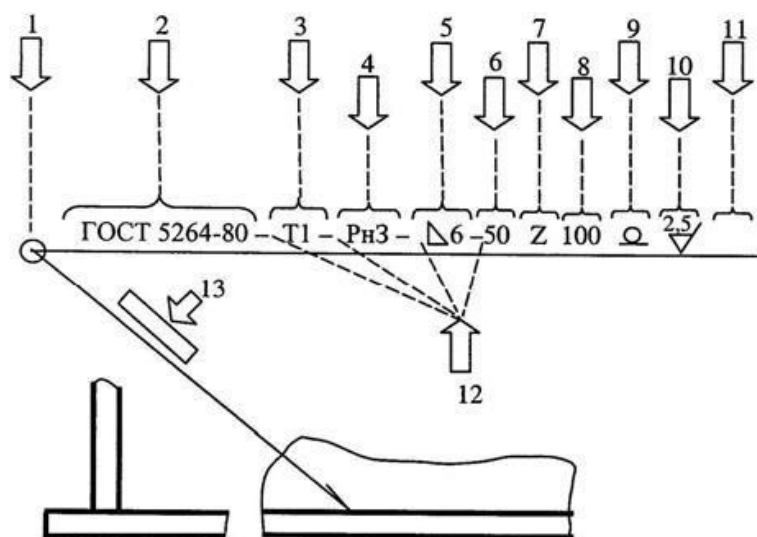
Структура обозначения шва: 1 – шов по замкнутому контуру; 2 – номер стандарта; 3 – буквенно-цифровое обозначение шва: Т1 – тавровый, односторонний; 4 – способ сварки: РнЗ – ручная электродуговая неплавящимся электродом в защитных газах; 5 – катет шва и его размер: К=6 мм; 6...8 – шов прерывистый шахматный длиной 50 мм и шагом 100 мм; 9 – усиление шва снять; 10 – шероховатость поверхности; 11 – место для знака, что шов выполнен по незамкнутой линии; 12 – дефис; 13 – указание о контроле шва
